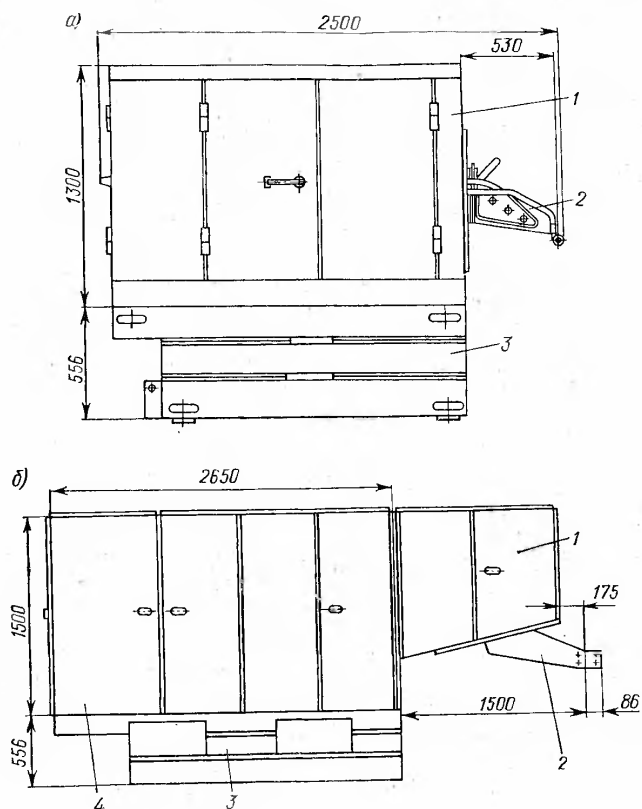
Сварочные устройства установок мощностью: а — 160 кВт; б — 400, 630, 1000 кВт;
